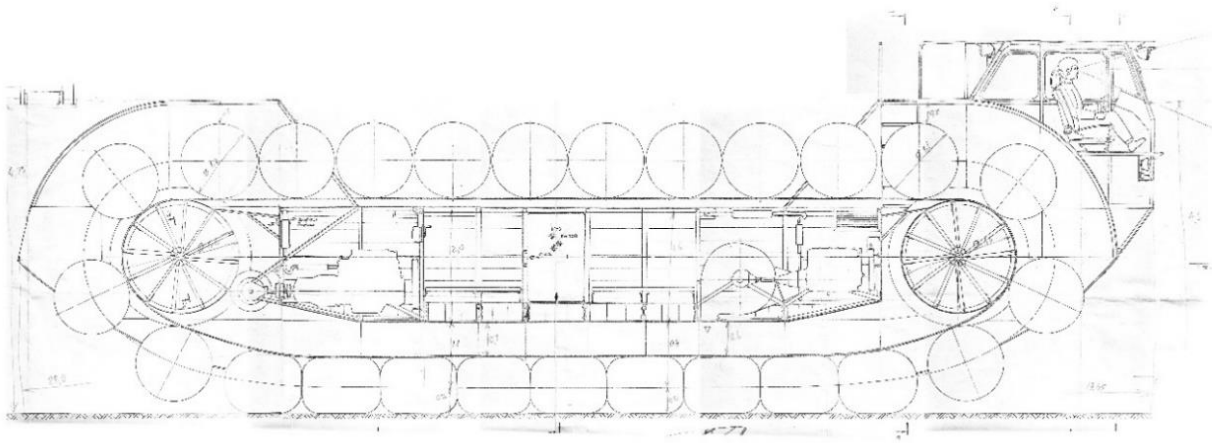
Боковой вид и размеры пневмоплицы ТСВГ-20.
